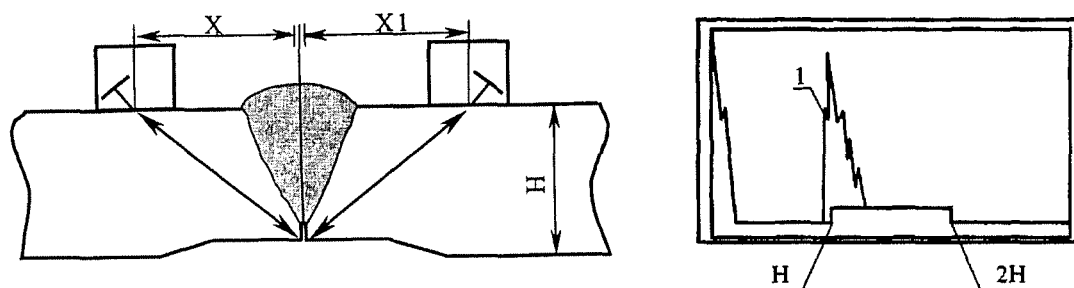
Сварное соединение со смещением кромок
